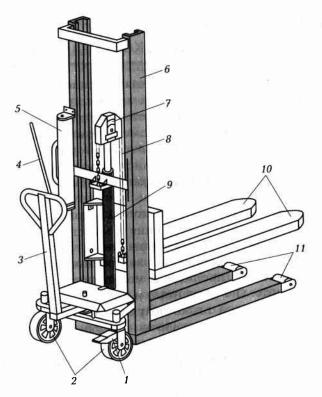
Высокоподъемный штабелер с гидравлическим подъемом вил: 1- тормоз; 2- передние колеса; 3- рукоятка перемещения; 4- рукоятка гидронасоса; 5- гидронасос; 6- рама; 7- звездочка; 8- цепь; 9- гидроцилиндр; 10- вилы; 11- задние колеса
